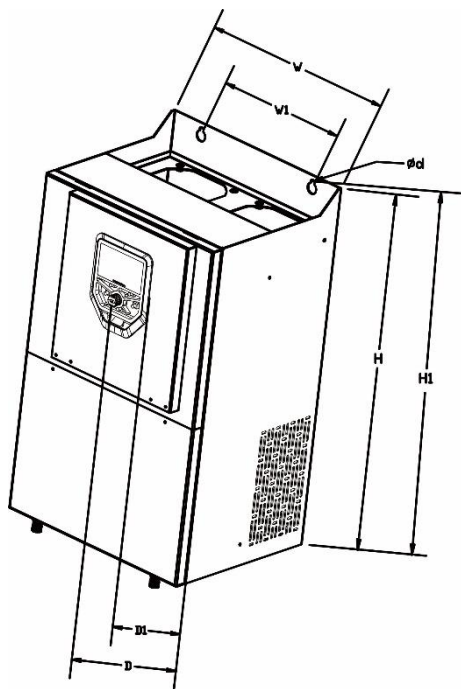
H330 系列 11kW-400kW 外型尺寸及安装尺寸示意图
